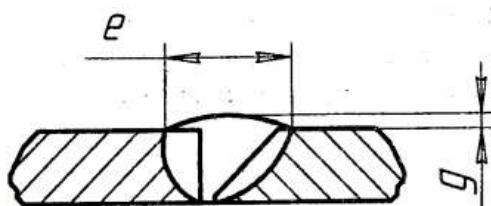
Конструктивные элементы сварного шва
